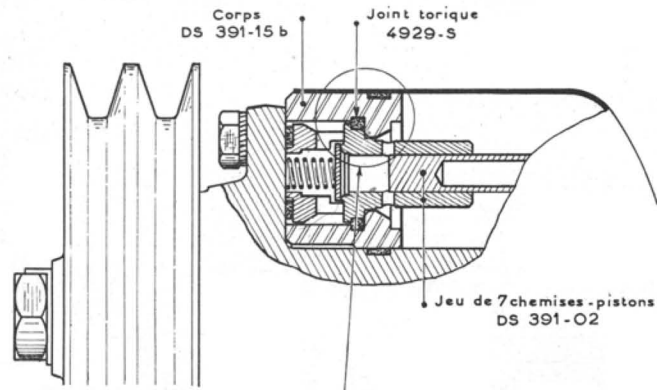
Vue en coupe du corps de pompe DS 391-15 b montrant une chemise à joint torique
